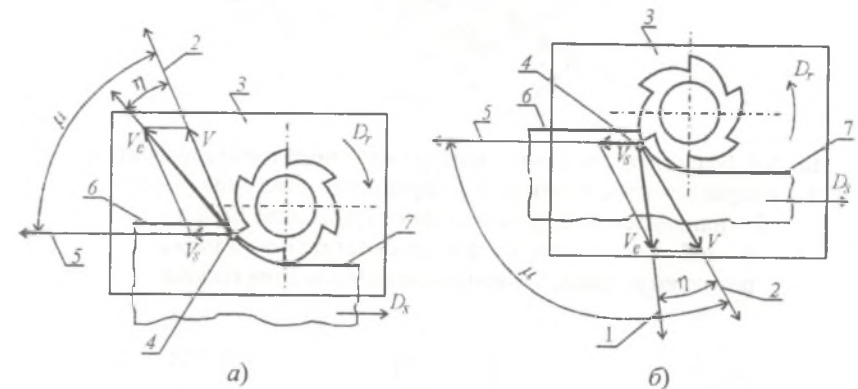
Элементы движений в процессе резания при цилиндрическом фрезеровании: а – при встречном фрезеровании; б – при попутном фрезеровании; 1 – направление скорости результирующего движения резания; 2 – направление скорости главного движения резания; 3 – рабочая плоскость P_s ; 4 – рассматриваемая точка режущей кромки; 5 – направление скорости движения подачи; 6 – обрабатываемая поверхность; 7 – обработанная поверхность
